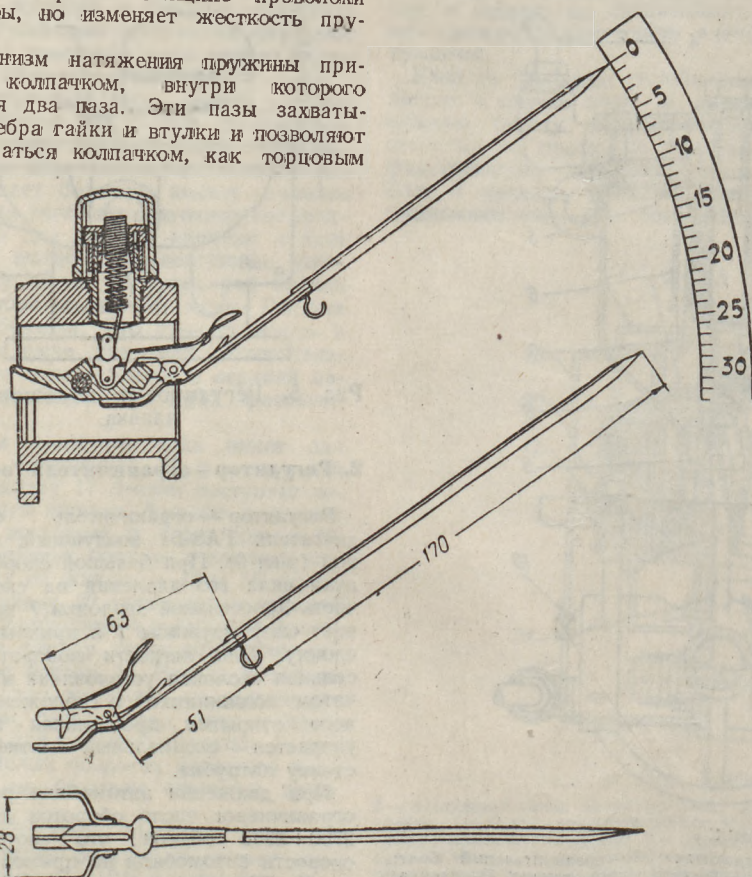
Схема прибора для проверки регулятора и эскиз стрелки.
